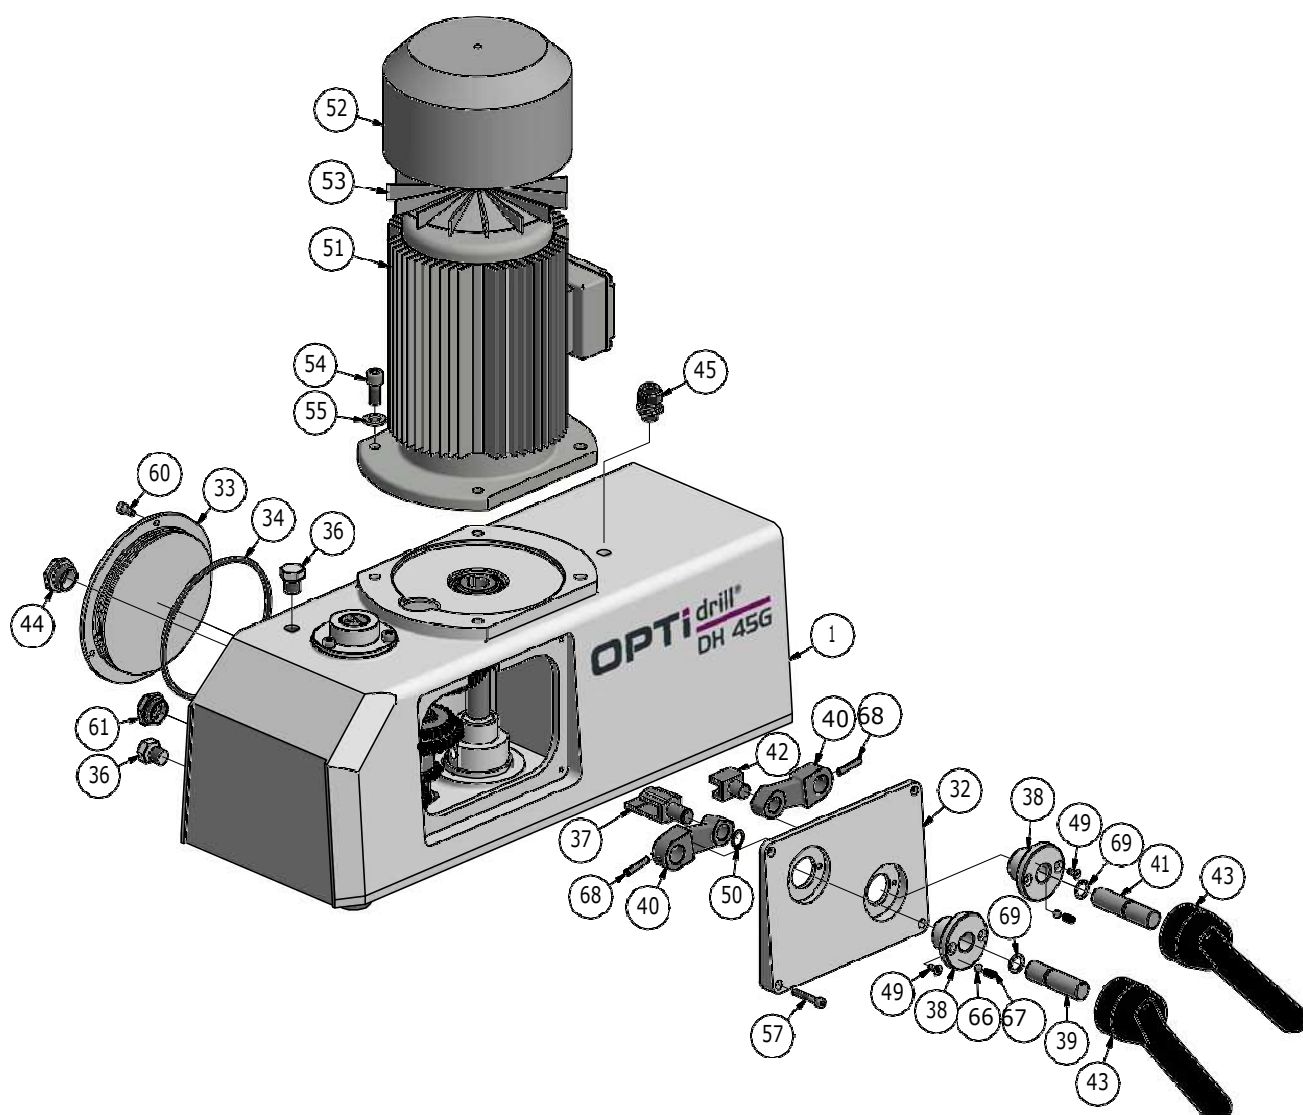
GetriebeTeil A - Elemento de engranaje A
